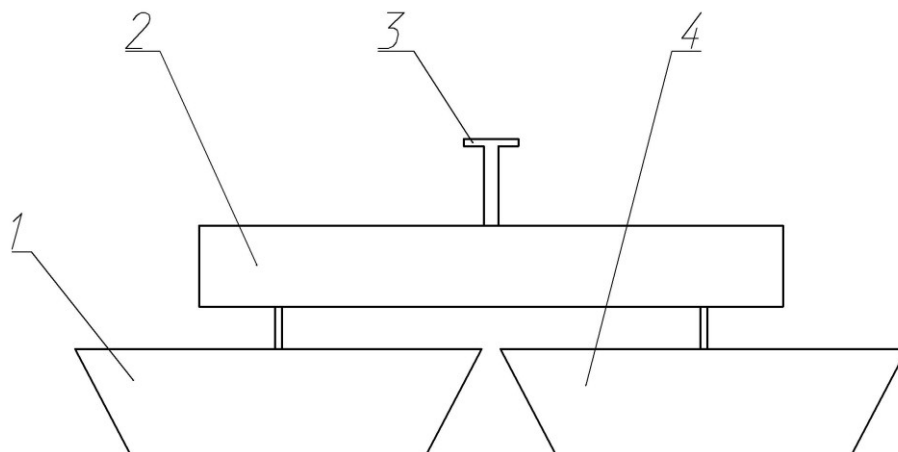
Кинематическая схема пожарного насоса НЦПН - 100/100: 1 – центробежная ступень; 2 – редуктор привода; 3 – фланец привода; 4 – центробежная ступень.
